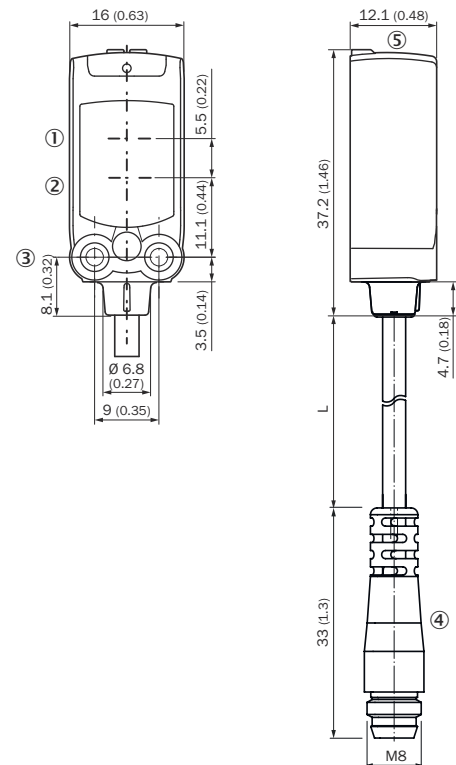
Disegno dimensionale, cavo con connettore maschio M8
